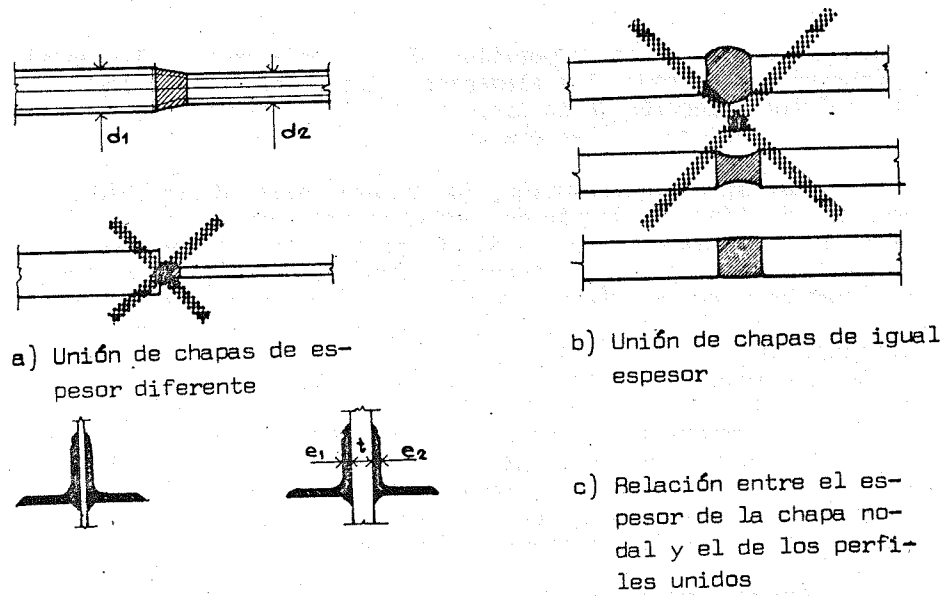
Reglas básicas para las uniones soldadas
